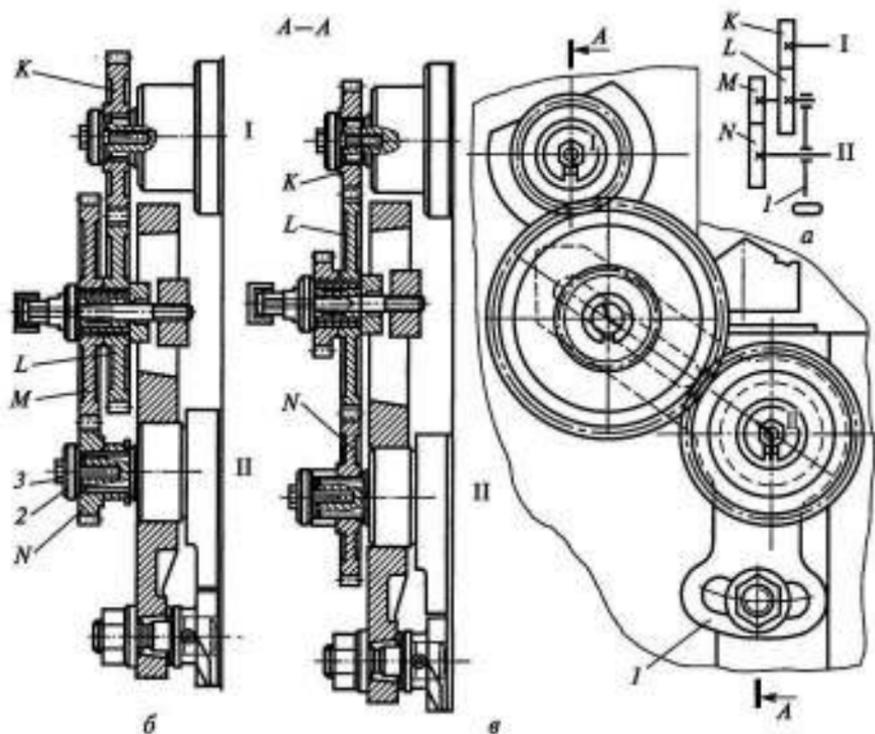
Кинематическая схема (а) и конструкция (б и в) гитары сменных зубчатых колес:
